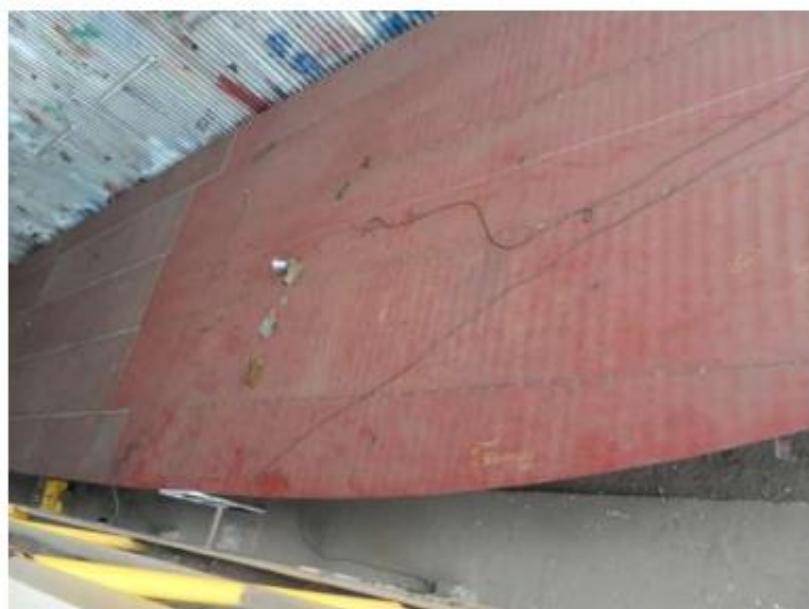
Convés principal da embarcação 653 já montado e parcialmente soldado.
